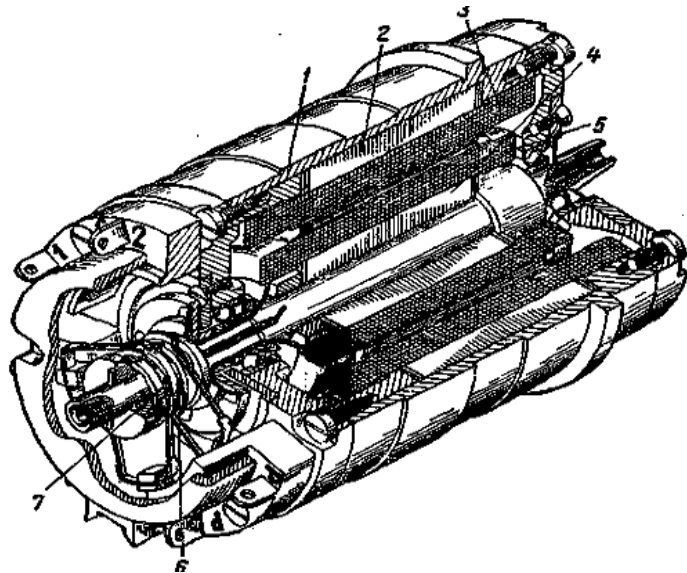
Вращающийся трансформатор: 1 – корпус; 2 – статор;
